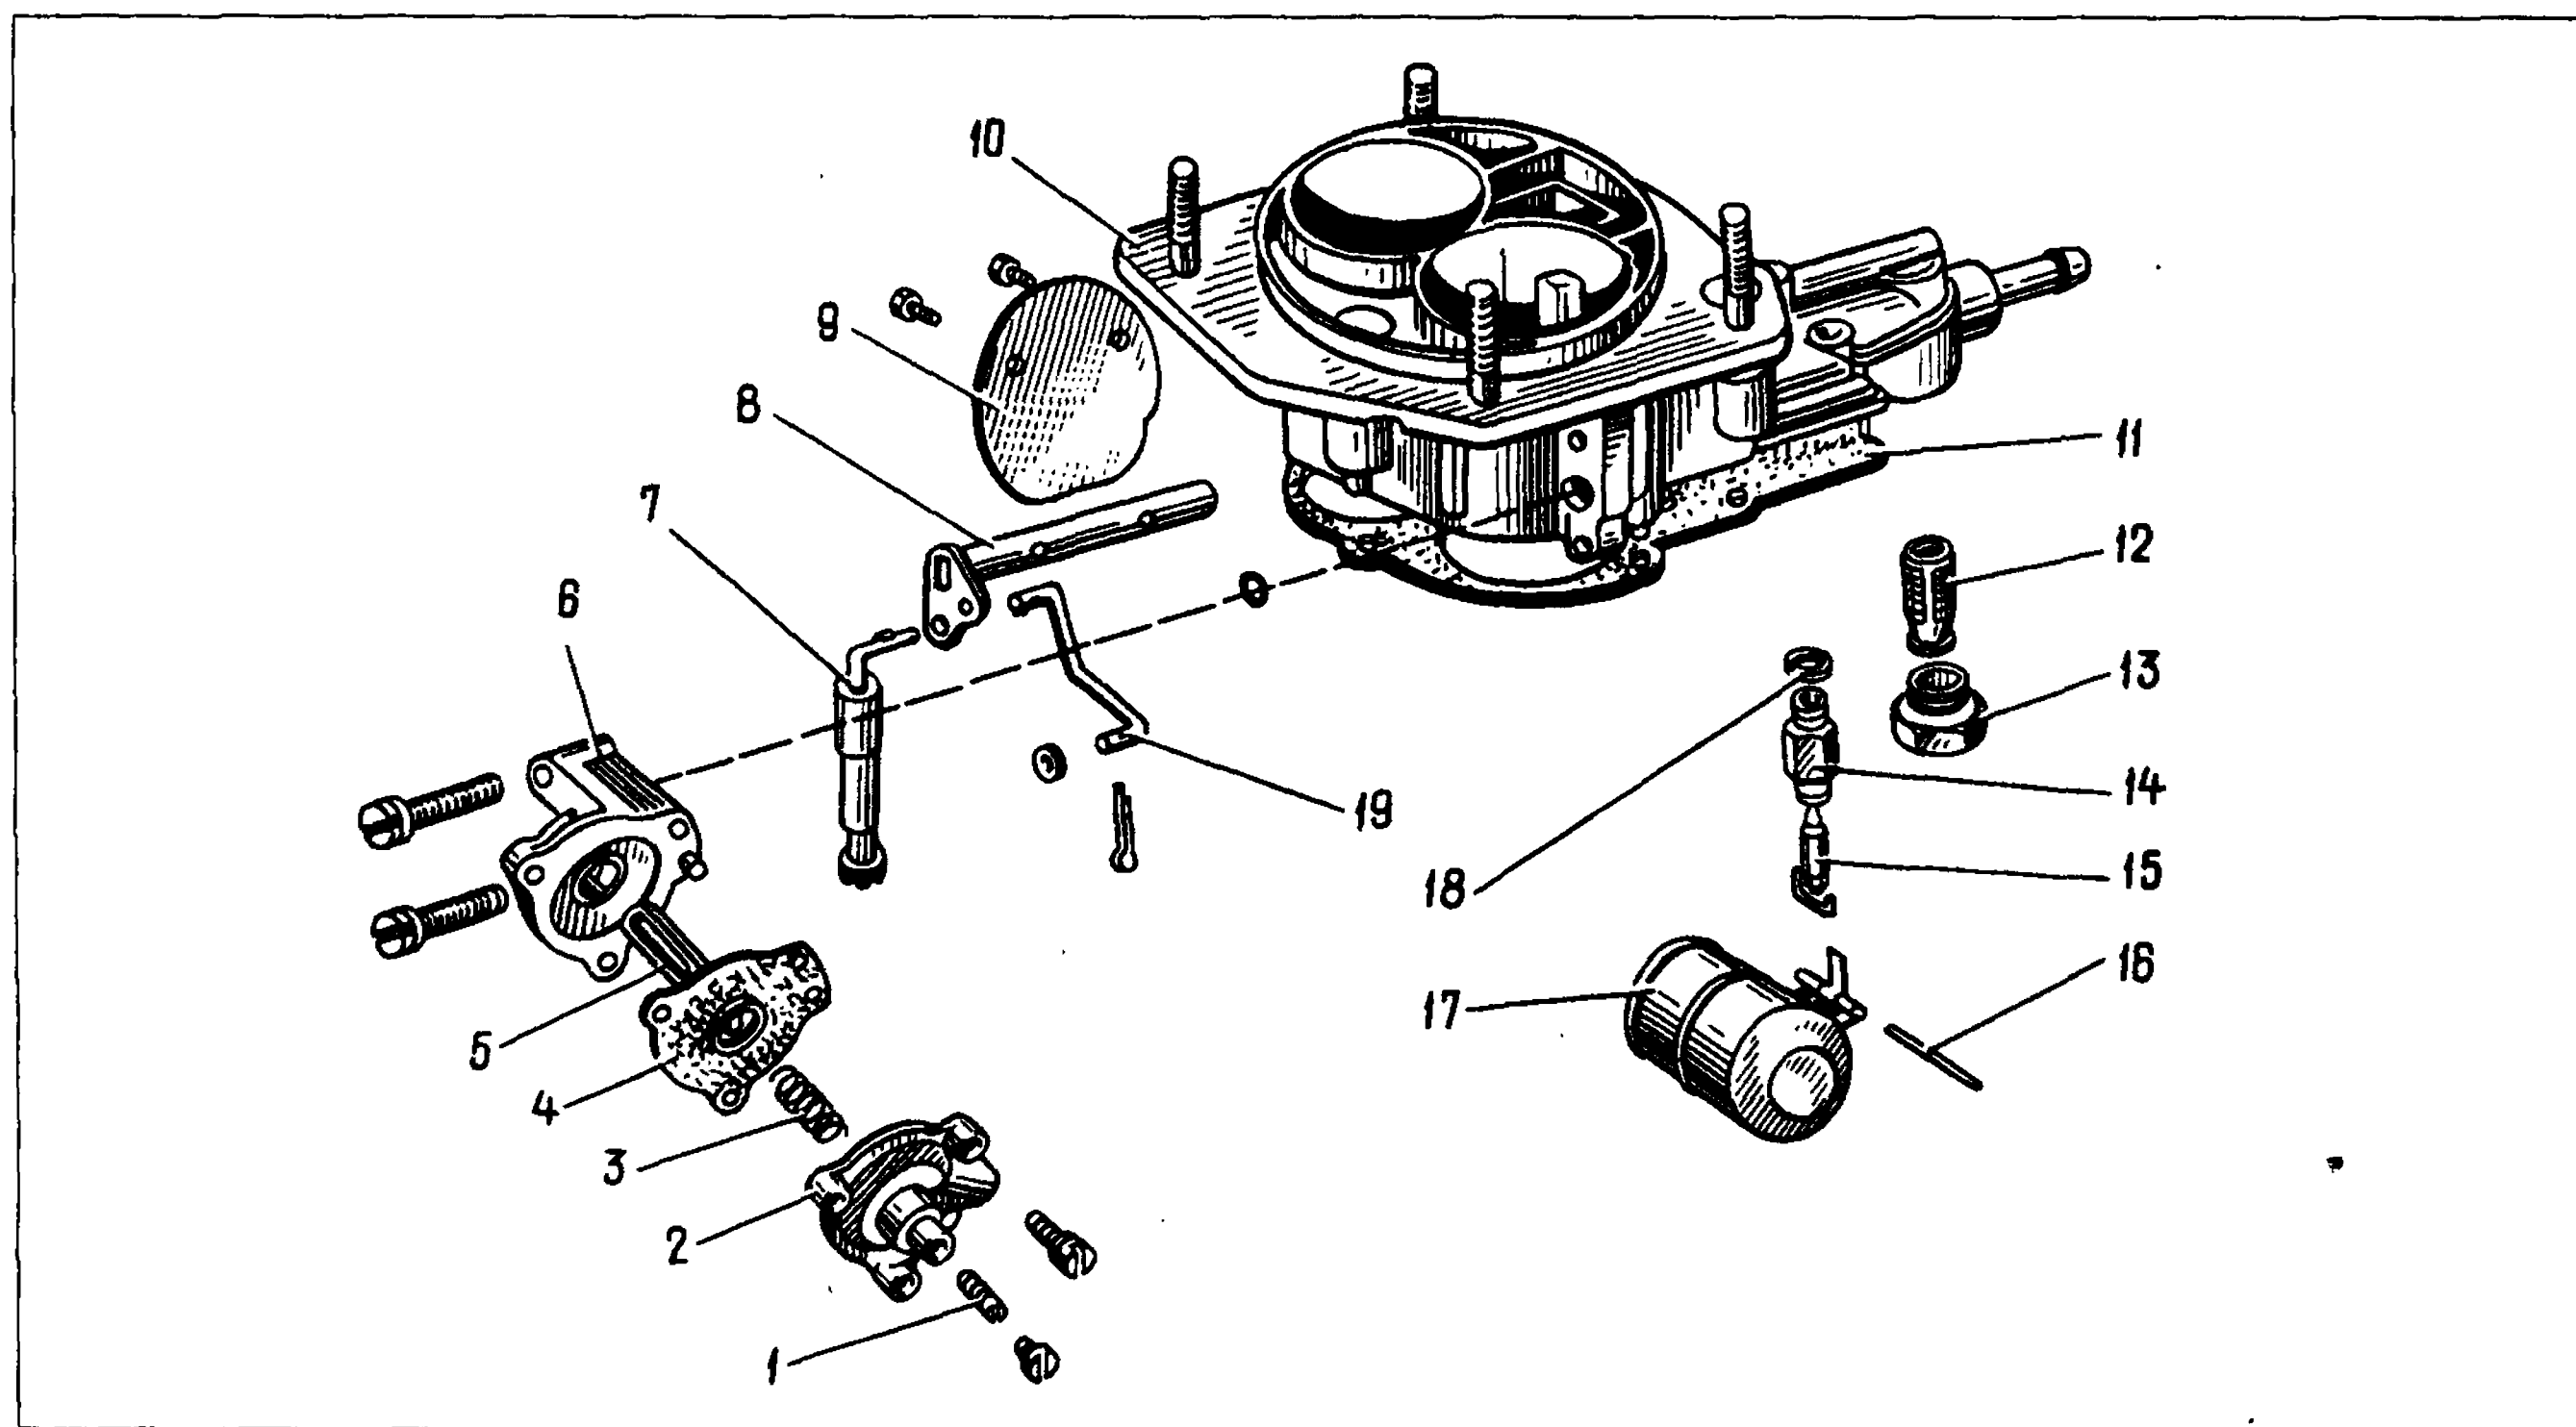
Детали крышки карбюратора 2107-1107010:
